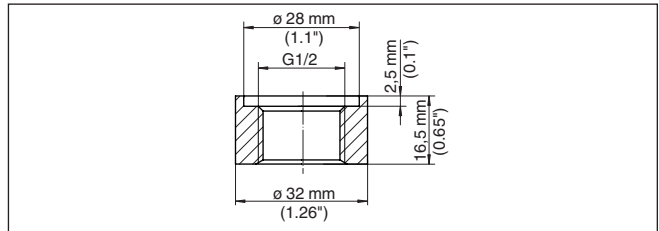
Maße Einschweißstutzen Gewinde G $\frac{1}{2}$ (DIN 3852-X)
